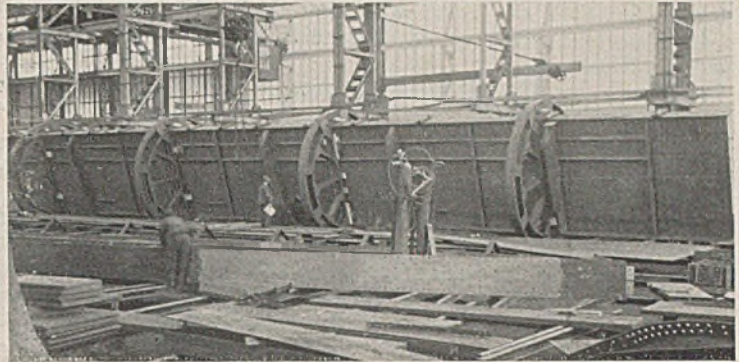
Drehvorrichtung für große geschweißte Brückenträger.
